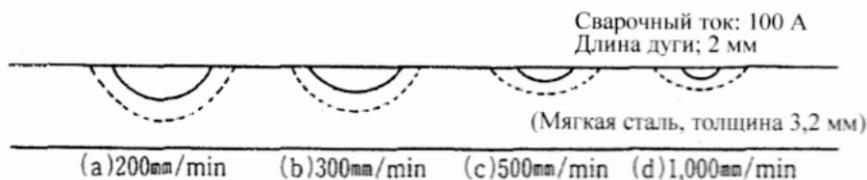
Влияние скорости сварки на форму валика
